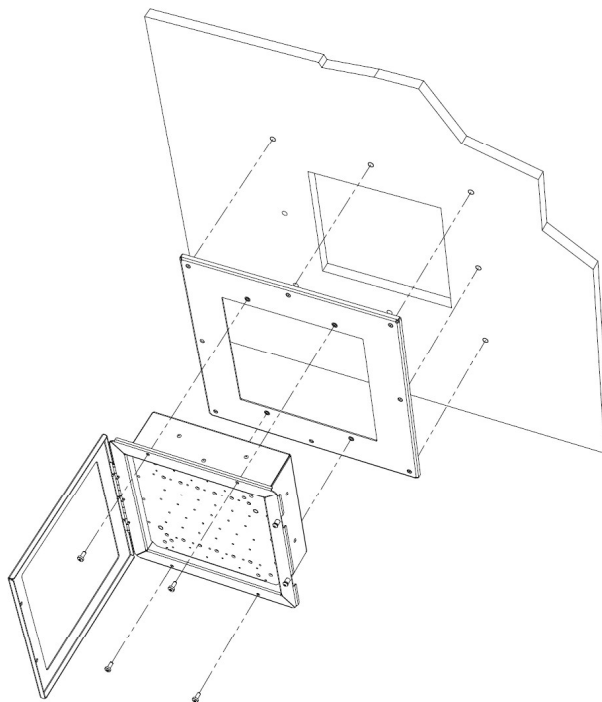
Figura C: Particolare sistema di fissaggio apparecchio pensilina
